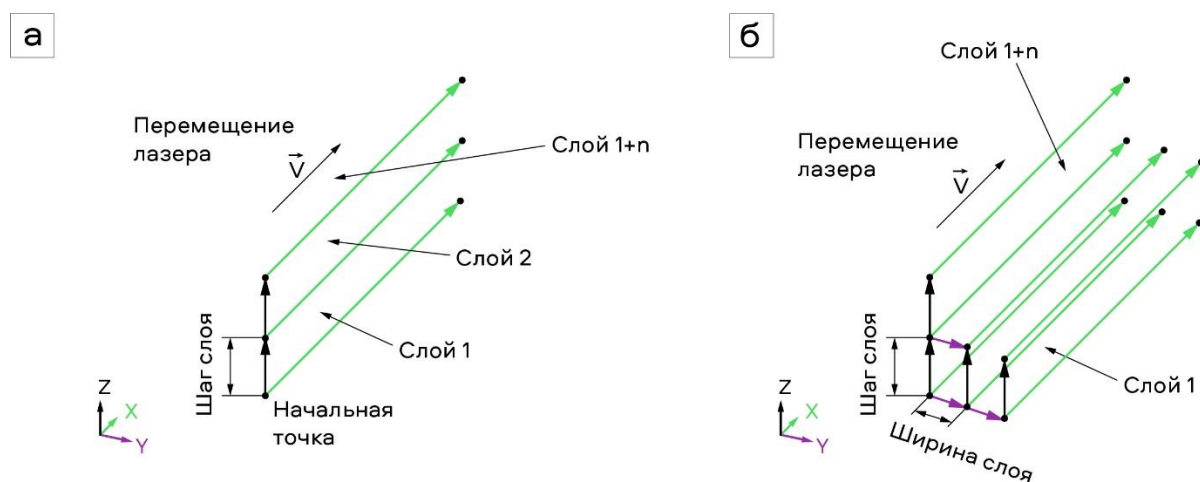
Схема перемещения рабочего инструмента. а – при послойной наплавке заготовки, состоящей из единичной стенки; б – при получении объемной заготовки
